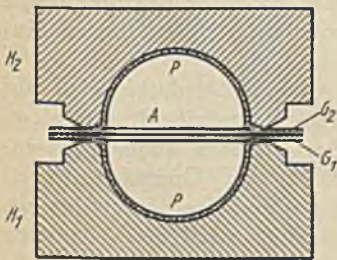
Zusammenschweißen der beiden Ballhälften
